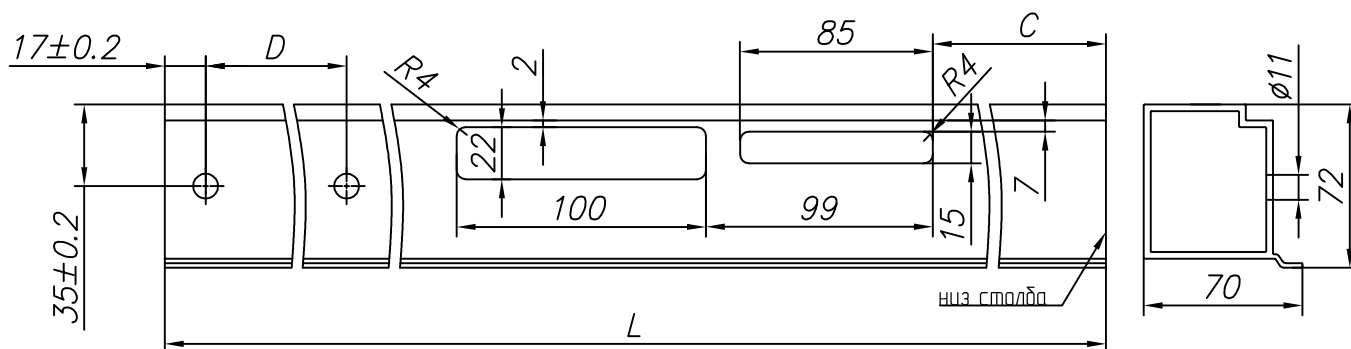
Изготовление столба притвора с пазом для автоматической защелки для калитки с левым открыванием (защелка 118WE)
